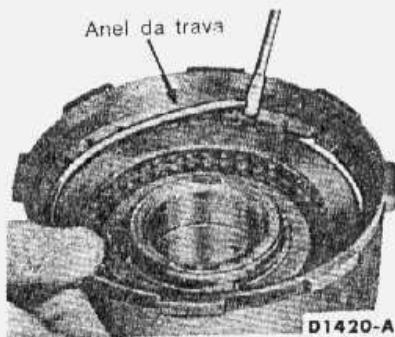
remoção do anel de trava da embreagem de ré e alta
